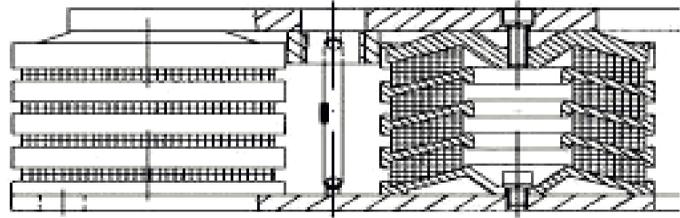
Конструкция демпфера с несколькими металлическими подушками
